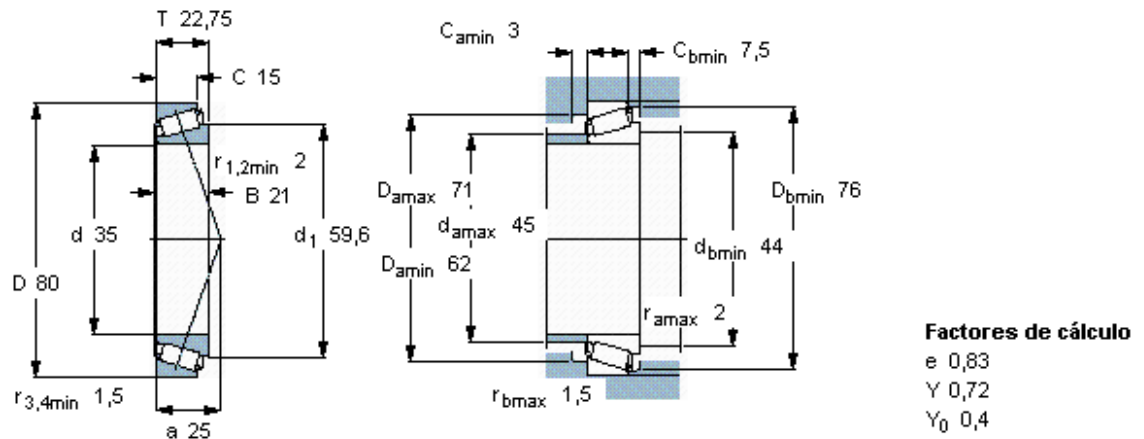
Dimensiones del Rodamiento 31307 J2/Q.
